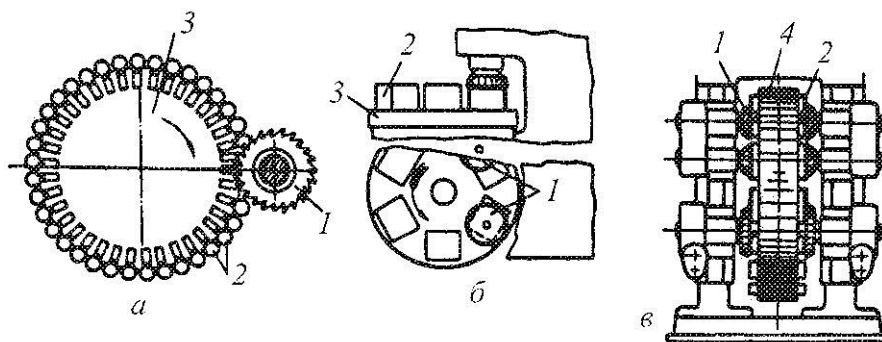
Фрезерування заготовок на фрезерних верстатах з безпервною круговою подачею
